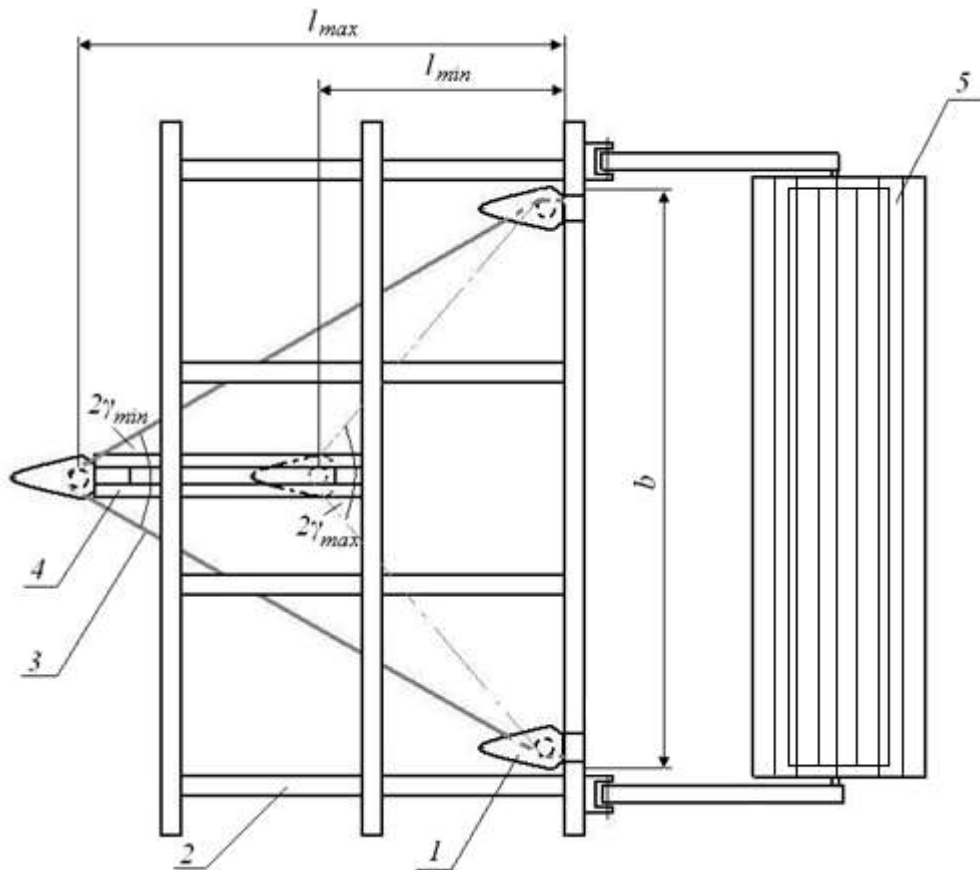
Конструктивна схема культиватора тросовокаткового
